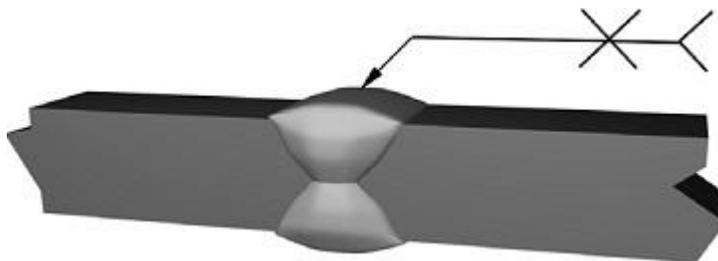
Unión por soldadura de tipo 1.
